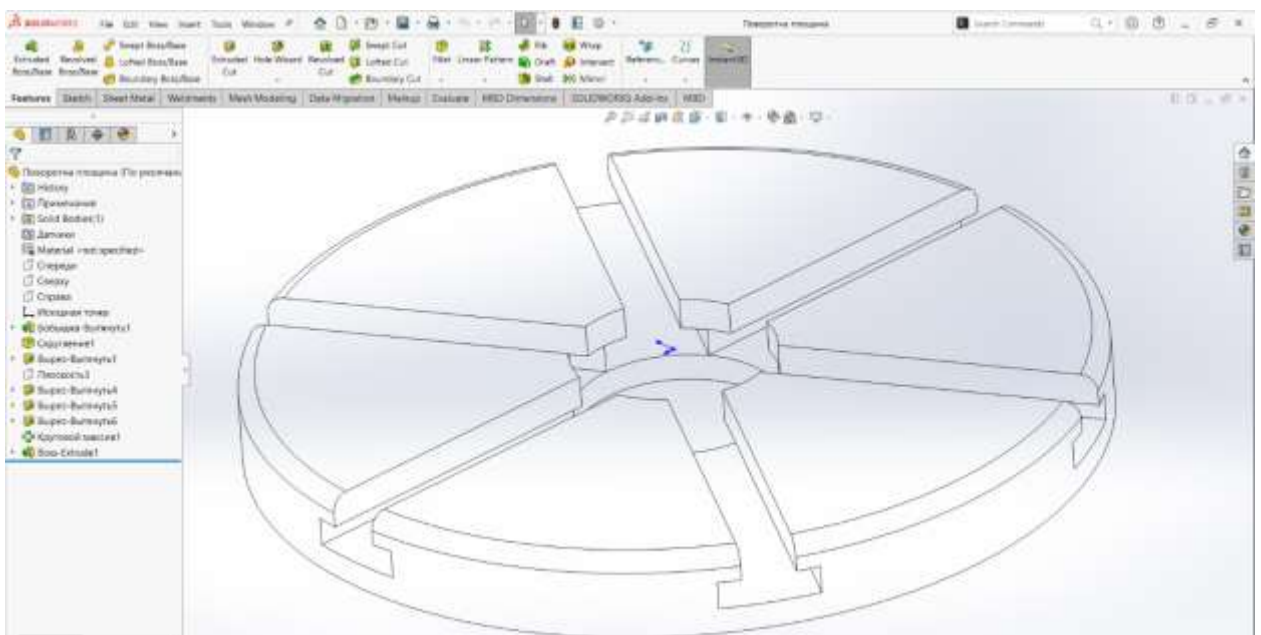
Змодельована деталь типу платформа поворотного столу
